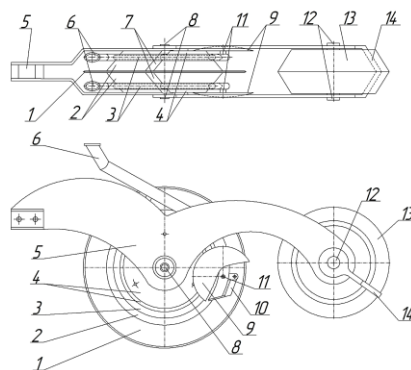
Комбинированный однодисковый сошник для узкорядного посева: 1 – плоский диск; 2 – реборда; 3 – бороздкообразователь; 4 – реборда; 5 – корпус; 6 – семянаправитель; 7 – чистик; 8 – ось; 9 – диск; 10 – клапан; 11, 12 – ось; 13 – прикатывающий каток; 14 – чистик
